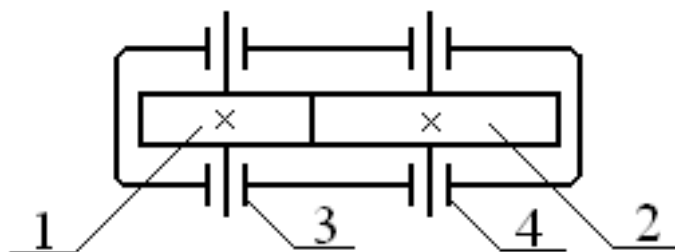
Схема редуктора цилиндрического одноступенчатого:
